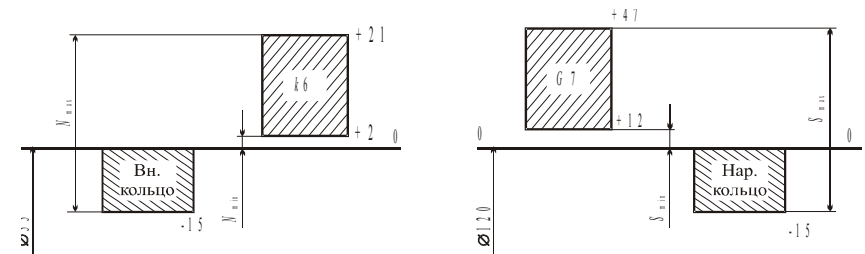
Схемы расположения полей допусков в соединении внутреннего кольца подшипника с валом и внешнего кольца с корпусом редуктора
